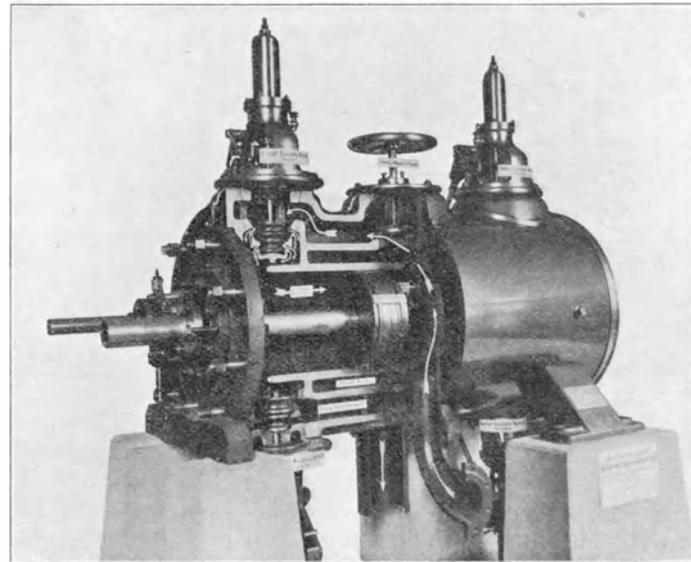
Geschnittener Zylinder einer Sulzerschen Ventilmaschine aus dem Jahre 1905. Die Dampfwege sind durch Pfeile gekennzeichnet
